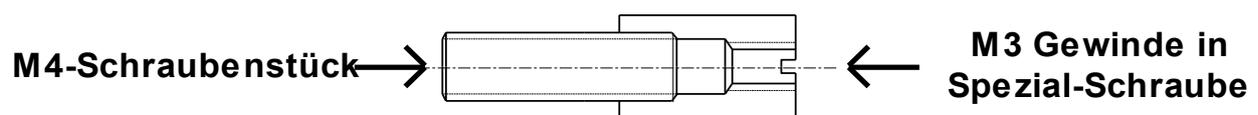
Detail der Frontplatten-Befestigung an den Gehäuse-Halbschalen
